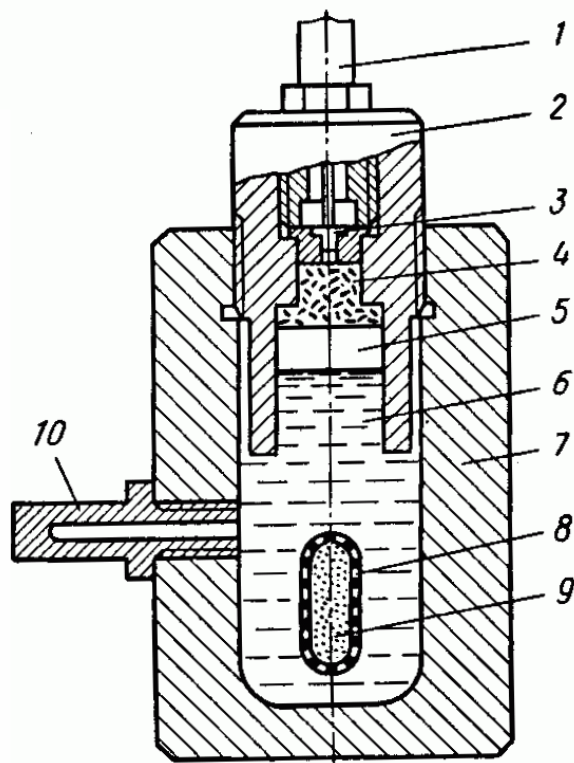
Схема установки для гидродинамического прессования: 1 – ударный механизм; 2 – боек; 3 – капсуль-жевало; 4 – пороховой заряд; 5 – поршень; 6 – рабочая жидкость; 7 – корпус установки; 8 – оболочка; 9 – порошок; 10 – манометр
